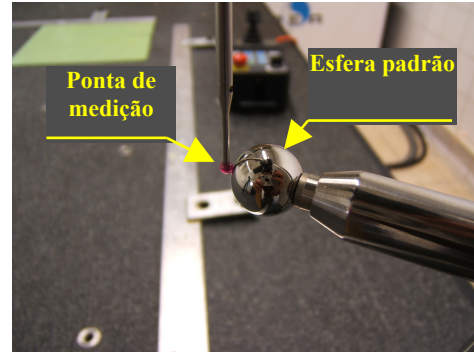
Medição de grandezas dimensionais e geométricas no LNEC
